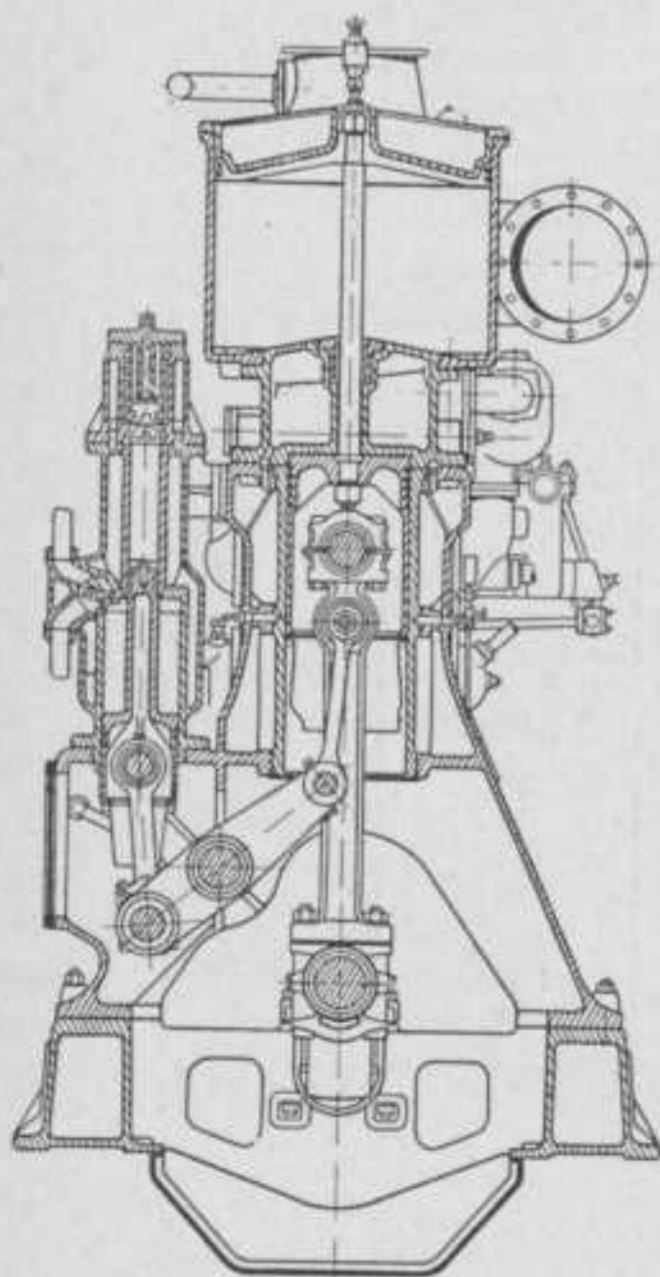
„Monte Penedo” motor, spool- en compressor-luchtpomp.
